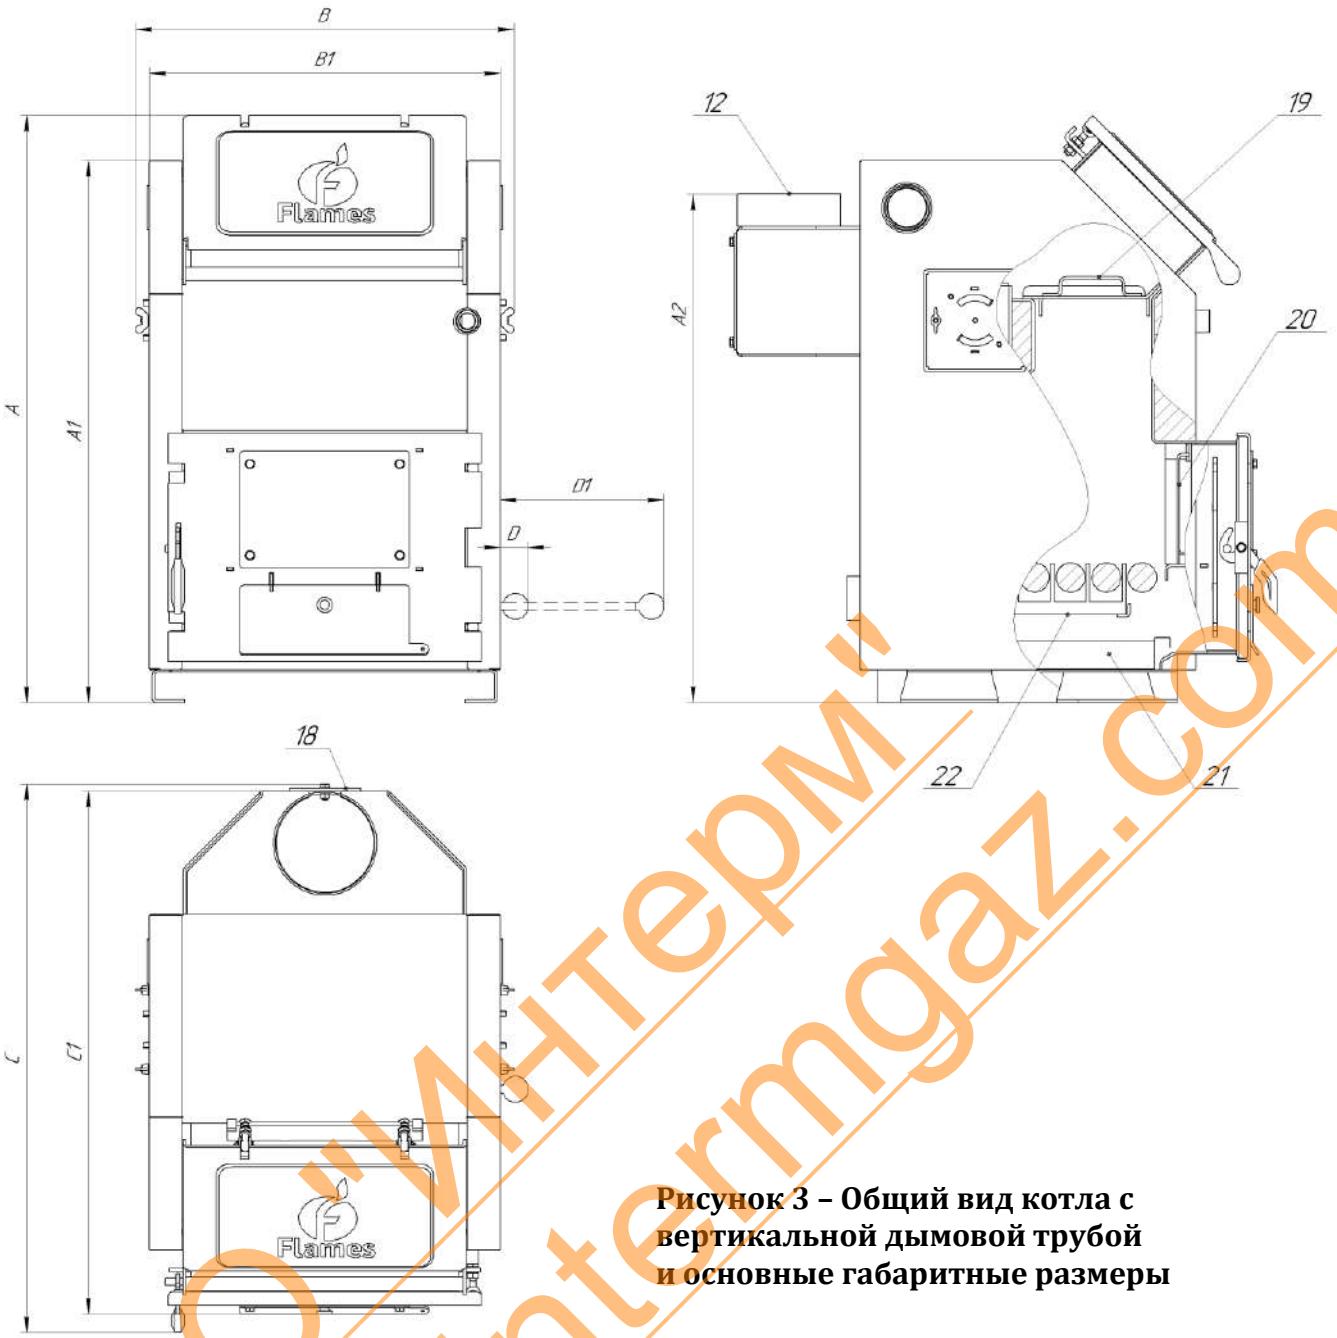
Общий вид котла с вертикальной дымовой трубой и основные габаритные размеры
